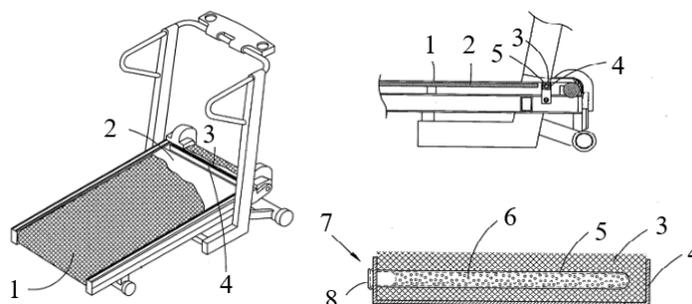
устройство смазочного аппарата для беговой дорожки
